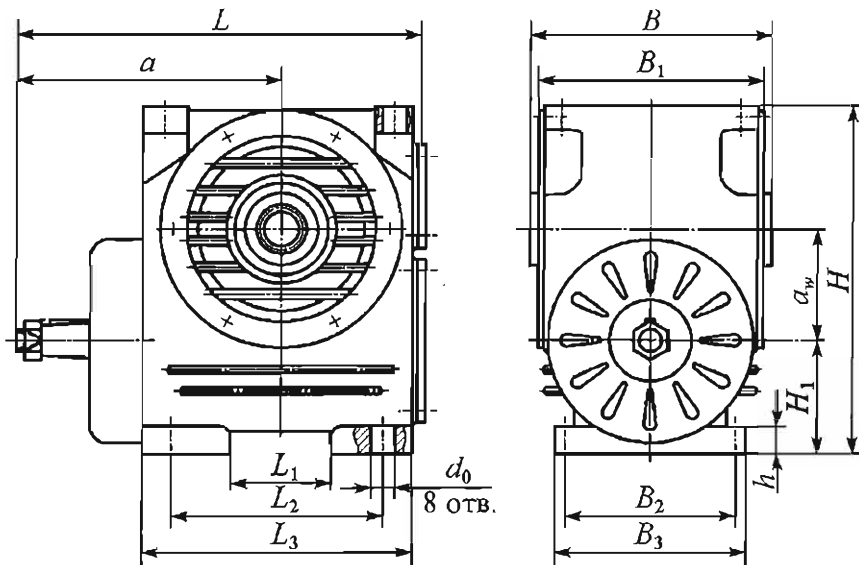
Габаритные, установочные и присоединительные размеры редуктора
